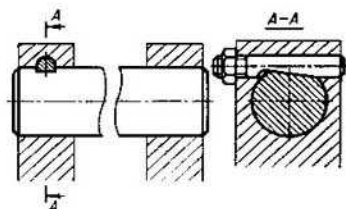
Fijación longitudinal y angular mediante un tornillo de apriete con rebajo plano cuneiforme
